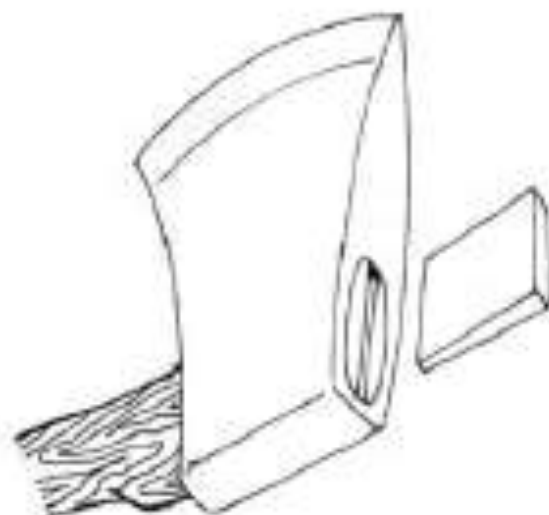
Detalhe da colocação da cunha de segurança da cabeça do machado
